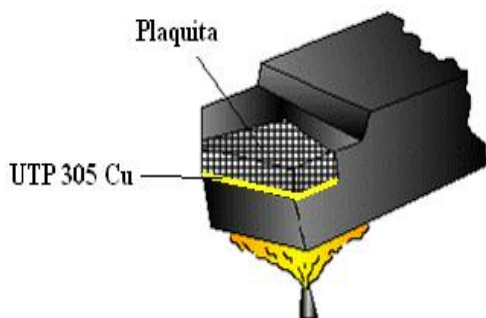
Procedimiento de soldadura de las cuchillas.
